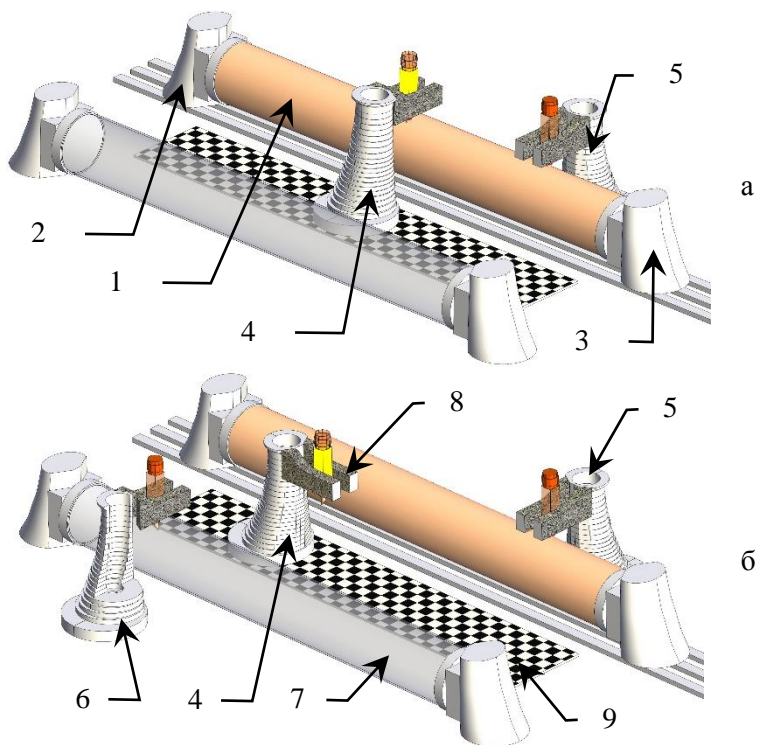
Компоновка аддитивно-субтрактивного станка для обработки деталей типа валов на двух параллельных позициях (1, 7) с разделением времени аддитивной бионической башни 4 и с позиционными субтрактивными башнями 5, 6: а – башни 4,5 обрабатывают деталь 1; б – башня 4 перемещается для обработки детали 7. 2, 3 – бабки; 8 – суппорт; 9 – станина башни
